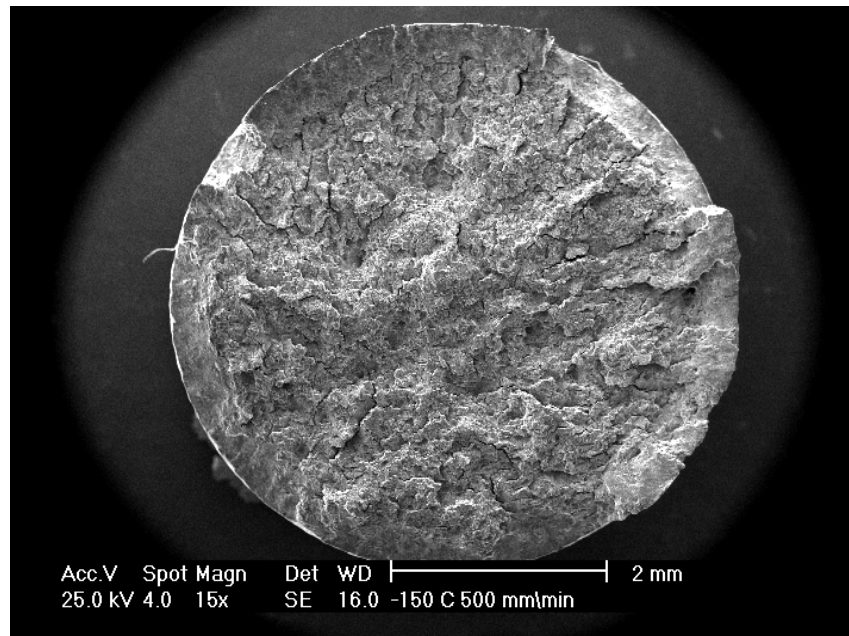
a: Superficie fracturada de la sección transversal de la probeta
